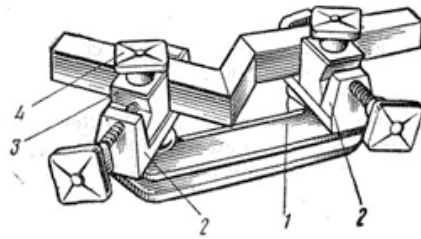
Универсальное приспособление для сварки мелких узлов:
